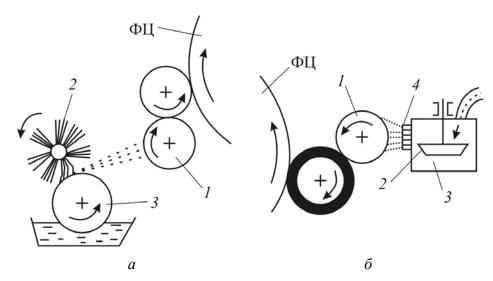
Контактные увлажняющие аппараты с бесконтактным питанием: a — щеточного типа: I — раскатной цилиндр; 2 — щетка; 3 — дуктор; δ — роторного типа; I — раскатной цилиндр; 2 — ротор; 3 — кожух; 4 — сетка; Φ Ц — формный цилиндр
